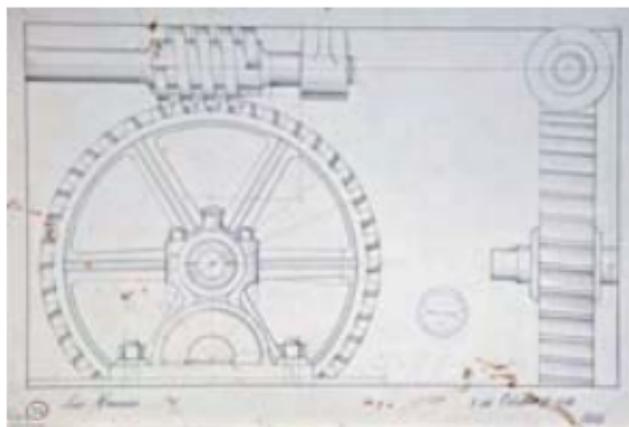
Proyecto de engranaje, alumno Luis Herrerías, clase de dibujo de máquinas, 1866
